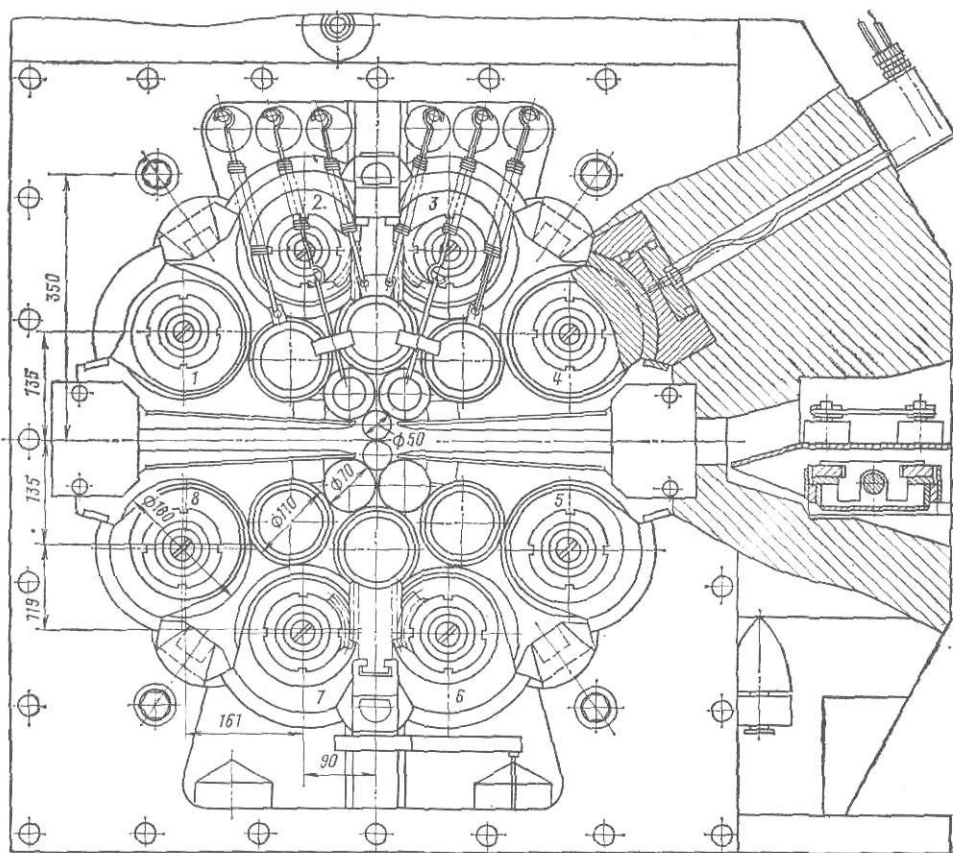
Рабочая клетка 20-валкового стана с длиной бочки 500 мм (1—8 — опорные ролики)
